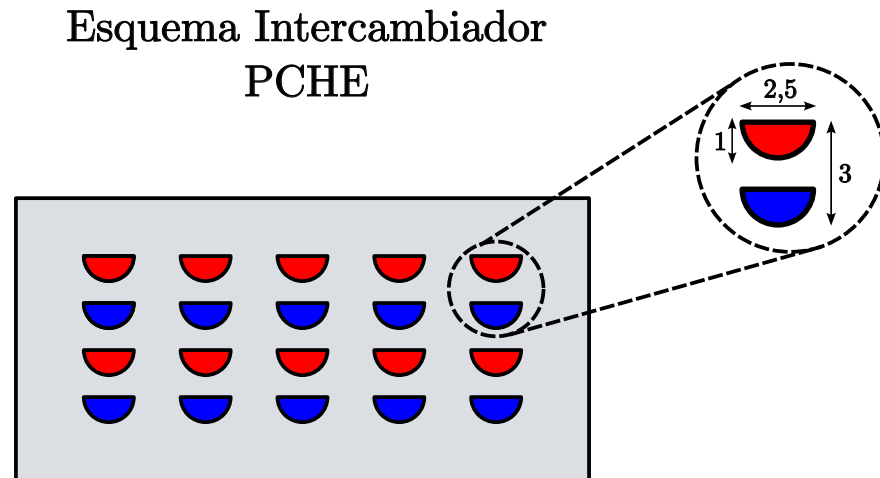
Croquis de un intercambiador PCHE. Dimensiones en [mm]
